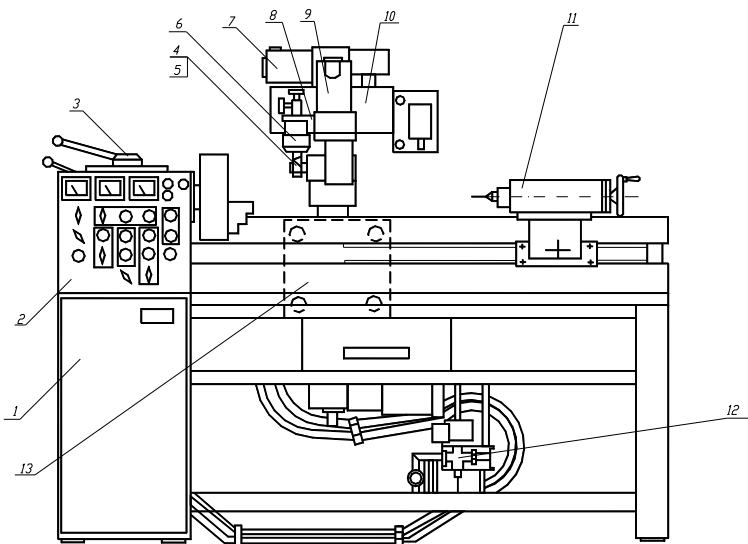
Загальний вид установки УД 417: 1 – станина; 2 – пульт керування; 3 – пристрій для обертання деталі; 4 – мундштук; 5 – притисний механізм; 6 – плазмотрон; 7 – коливальний привід; 8 – коректор; 9 – привід; 10 – наплавочна голівка; 11 – піноль; 12 – панель охолодження води; 13 – каретка
